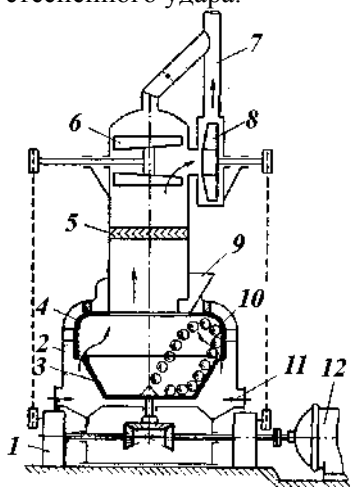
Центробежно-шаровая мельница: 1 – редуктор; 2 – корпус; 3 – чаша; 4 – размольное кольцо; 5 – отбойная решетка; 6 – сепаратор; 7 – выводной штуцер; 8 – вентилятор; 9 – штуцер питания; 10 – шары; 11 – штуцер для подвода газа-носителя; 12 – двигатель.
